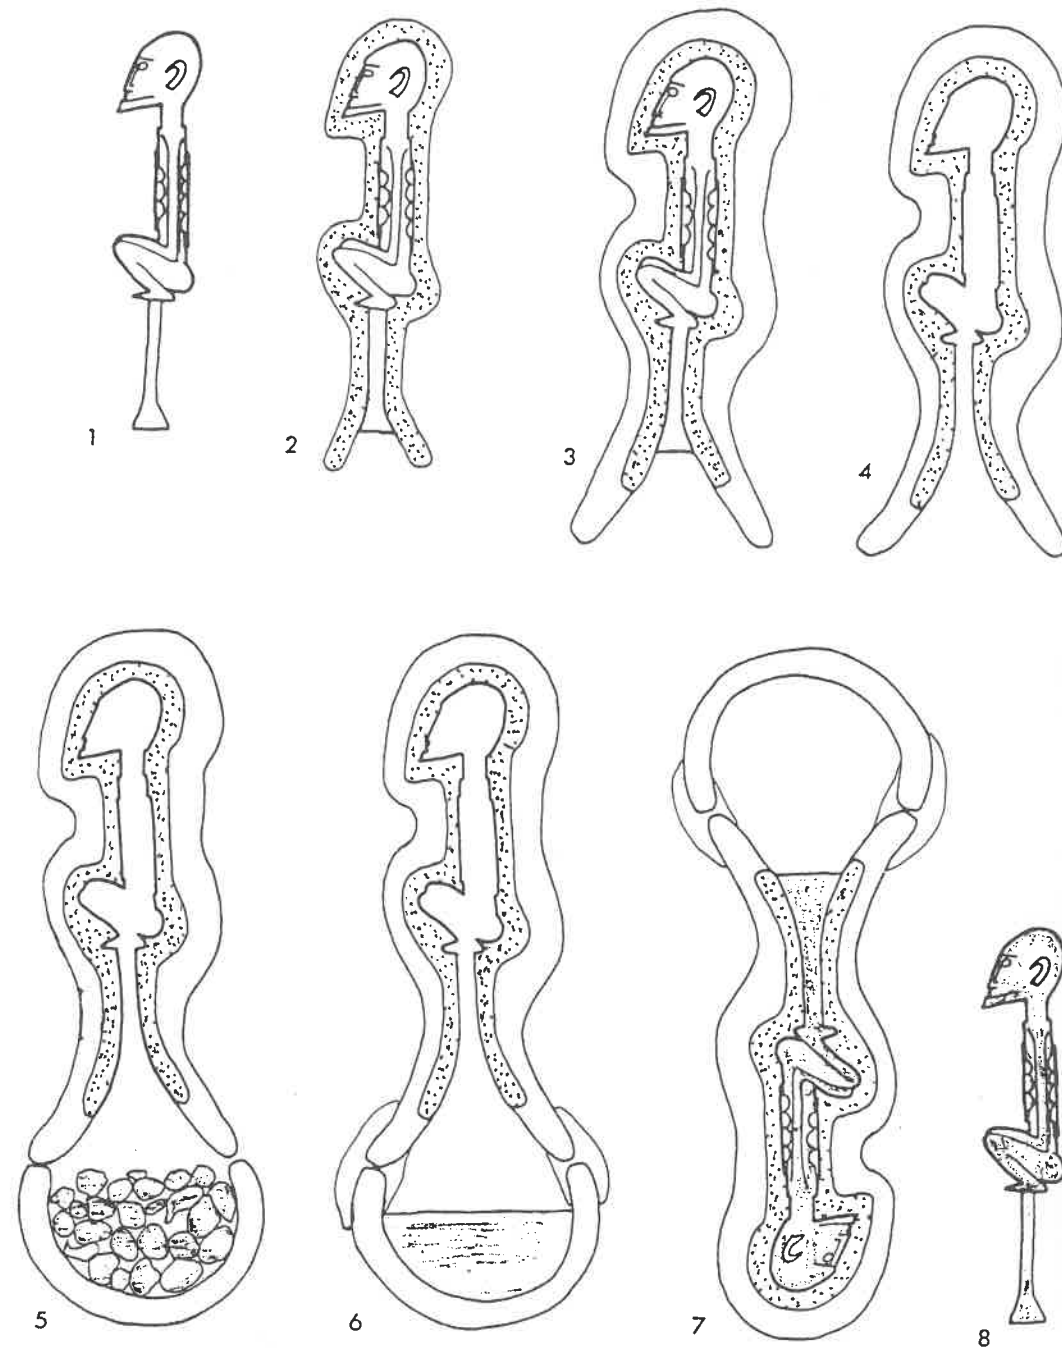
Schema zum Wachausschmelzverfahren im geschlossenen System:
